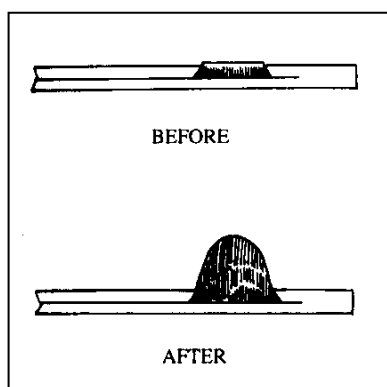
Forma correcta del montículo de soldadura.
